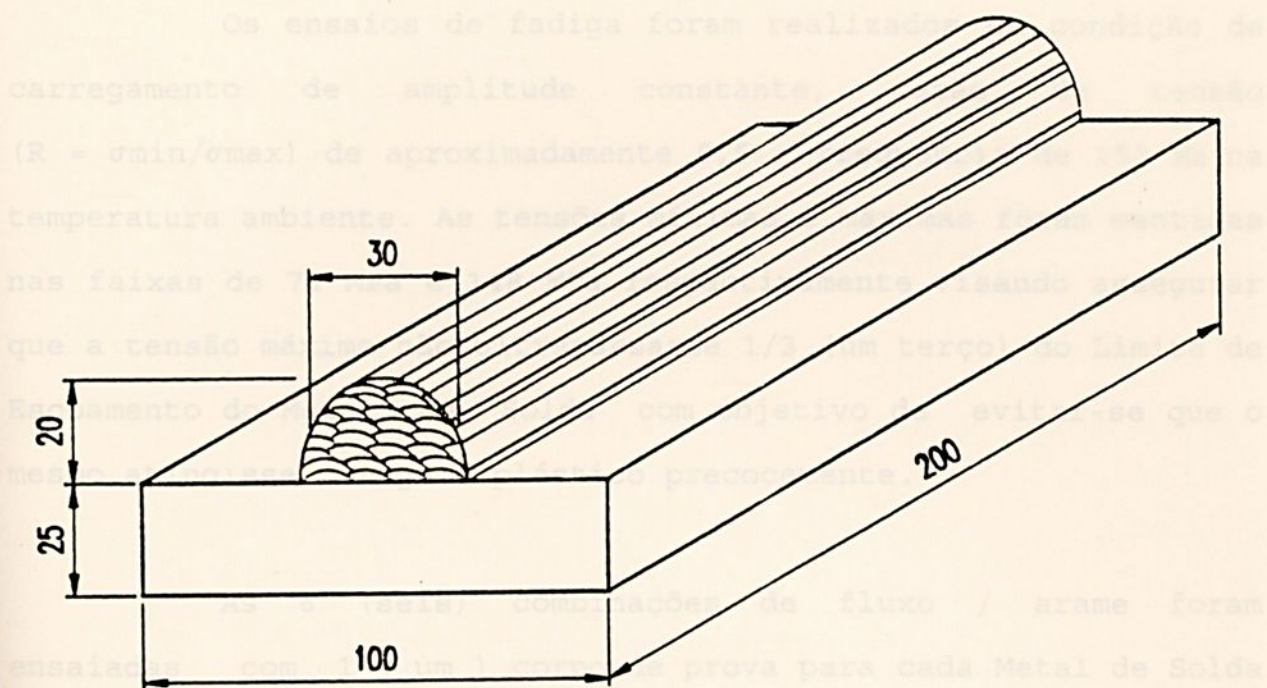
Corpo de Prova para Análise Química do Metal de Solda Não-Diluído
